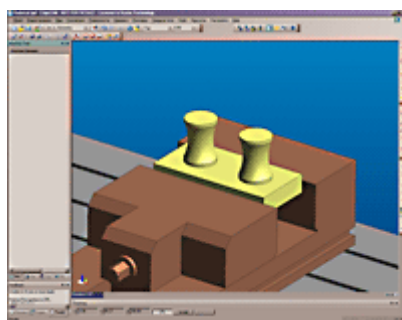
Модель детали полученной в Autodesk Inventor и загруженной в Edgcam.
